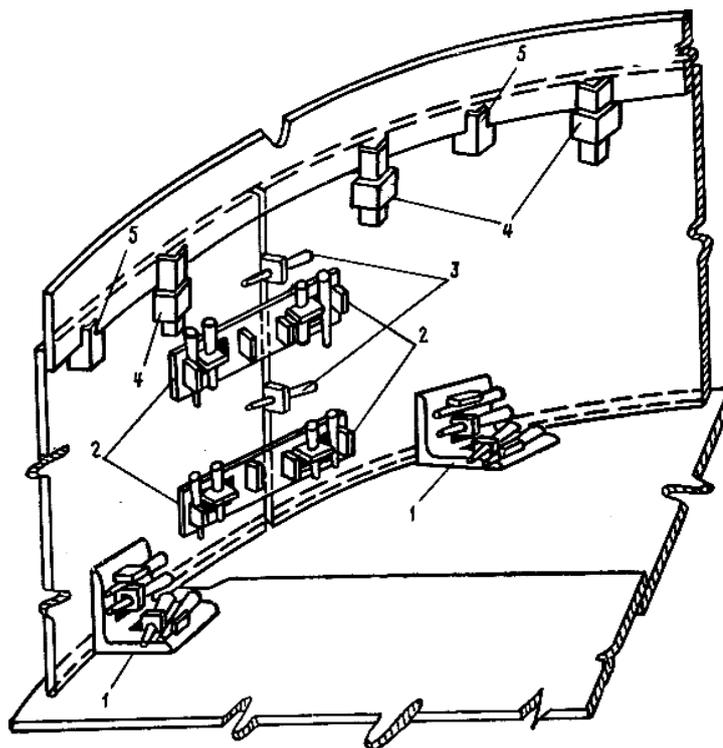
Этапы сборки окраек на подкладке при изготовлении дна вертикального резервуара
